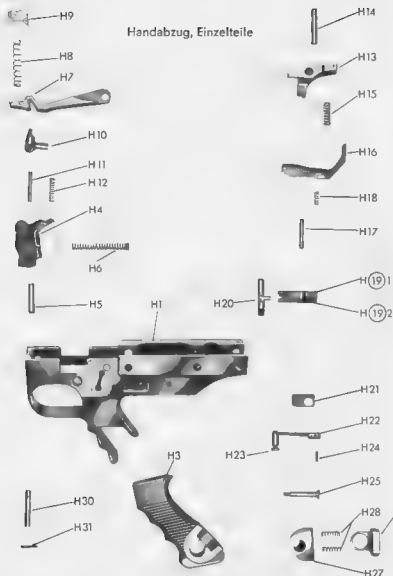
H1 = Griffstück, H3 = Griff, H4 = Abzug, H5 = Bolzen, H6 = Druckfeder, H7 = Abzugshebel, H8 = Druckfeder, H9 = Platte, H10 = Sperrhebel, H11 = Bolzen, H12 = Druckfeder, H13 = Abzugsriegel, H14 = Bolzen, H15 = Druckfeder, H16 = Winkelhebel, H17 = Zylinderstift, H18 = Druckfeder, H20 = Gabelbolzen, H21 = Lagerplatte, H22 = Sicherungshebel, H23 = Rastknopf, H24 = Spannhebel, H25 = Senkschraube, H26 = Schieber, H27 = Befestigungsstück, H28 = Druckfeder, H29 = Zweilochmutter, H30 = Zylinderstift, H31 = Spannstift
